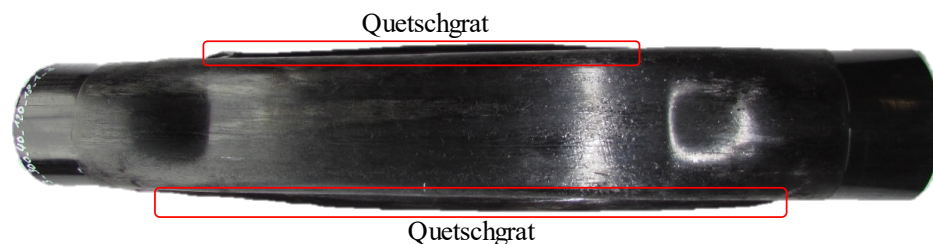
Quetschgrat bei der Umformung eines Halbzeugs mittels Abquetschwerkzeug
